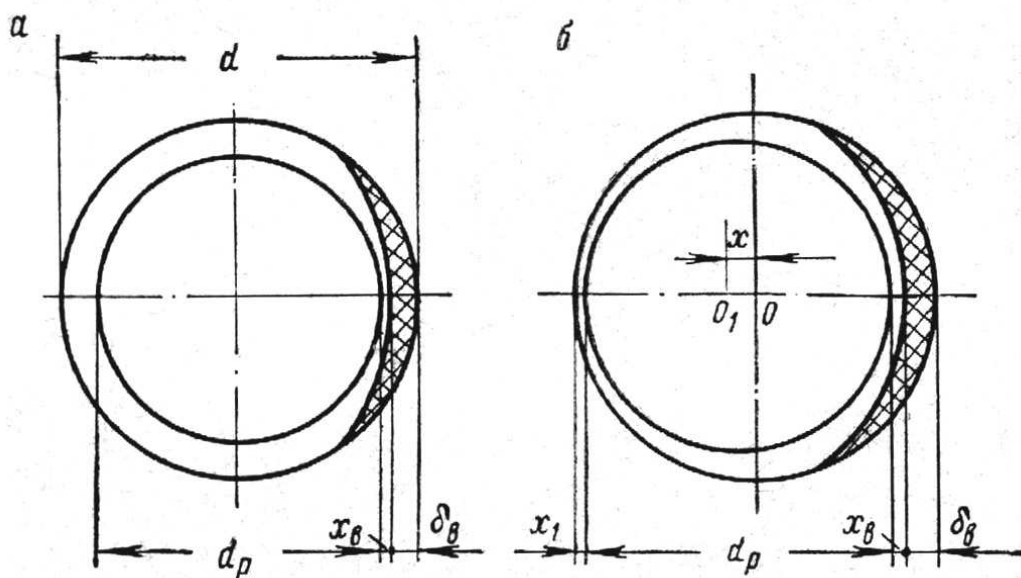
Размеры и допуски для обработки изношенного вала на ремонтный размер:
